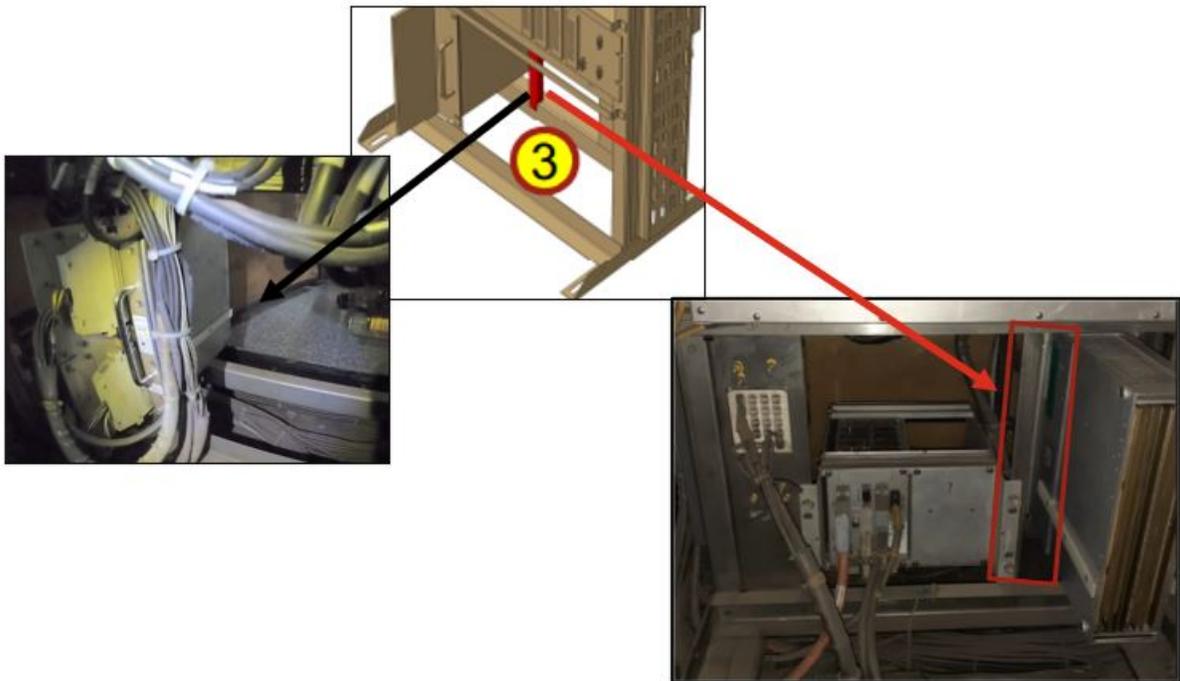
Soporte actual del procesador de la DDU que se debe remover.
